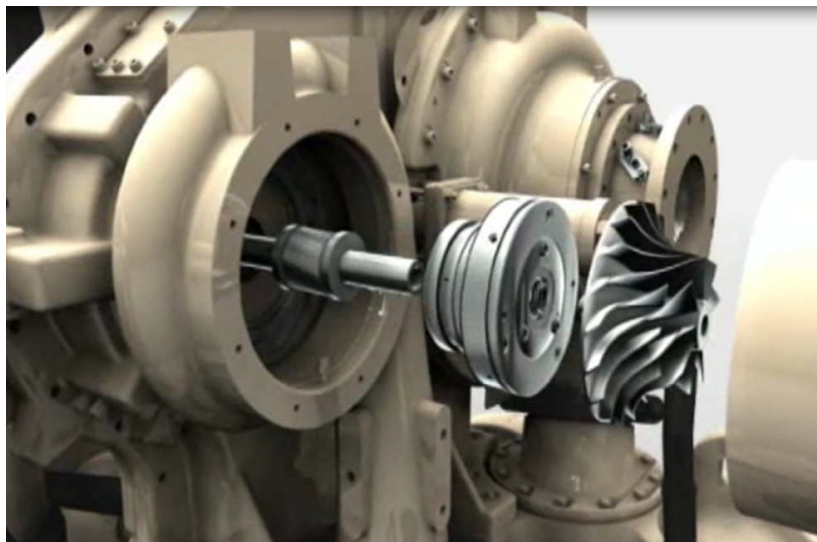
Vista explodida de compressor centrífugo Centac C1000 (Fonte: *Ingersoll-Rand*)
